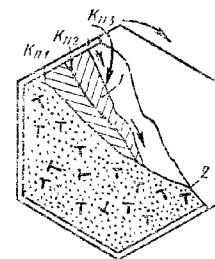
Схема процесса галтовки деталей в шестигранном барабане:
